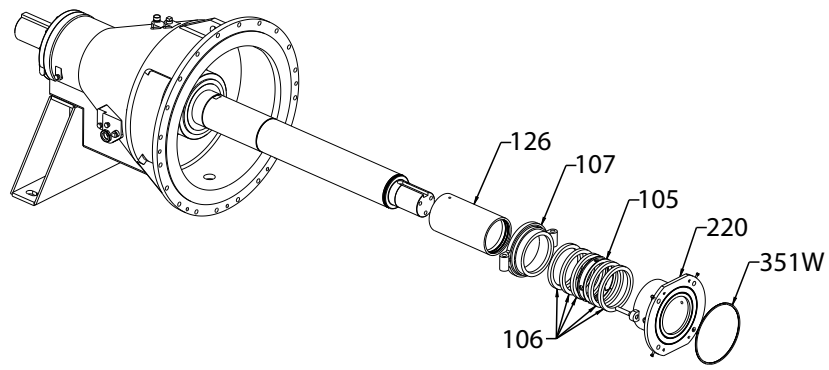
Extracción de la cámara, la empaquetadura y el anillo de cierre hidráulico
